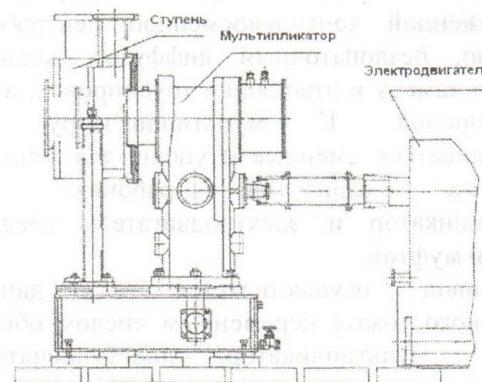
Стенд для испытания упорных подшипников скольжения
